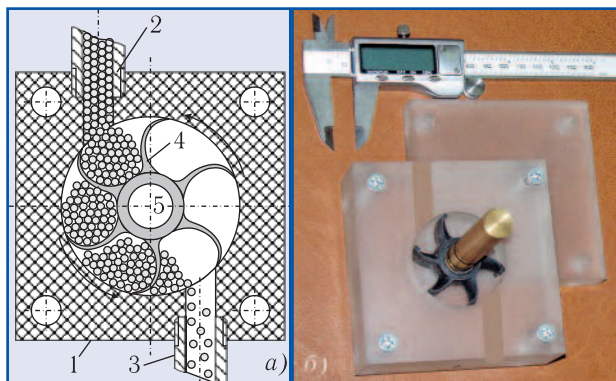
Конструктивное исполнение малорасходного дозатора сорбента (а) и его внешний вид (б): 1 — корпус; 2 — канал нагрева; 3 — горловина нижнего бункера; 4 — ротор с эластичными перегородками; 5 — вал привода
